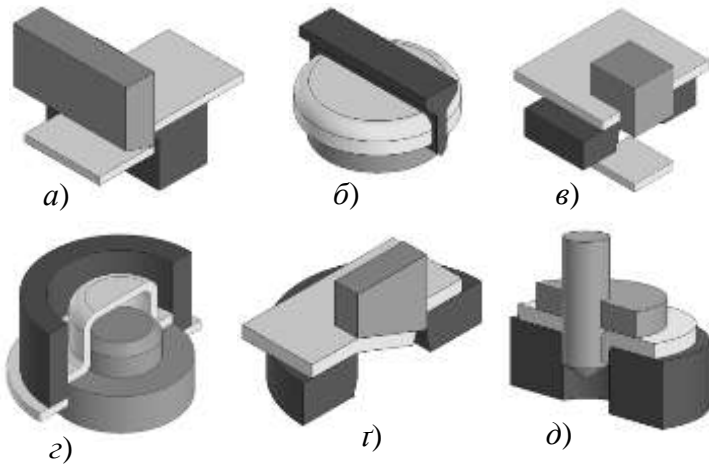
Роз'єднувальні операції холодного штампування
